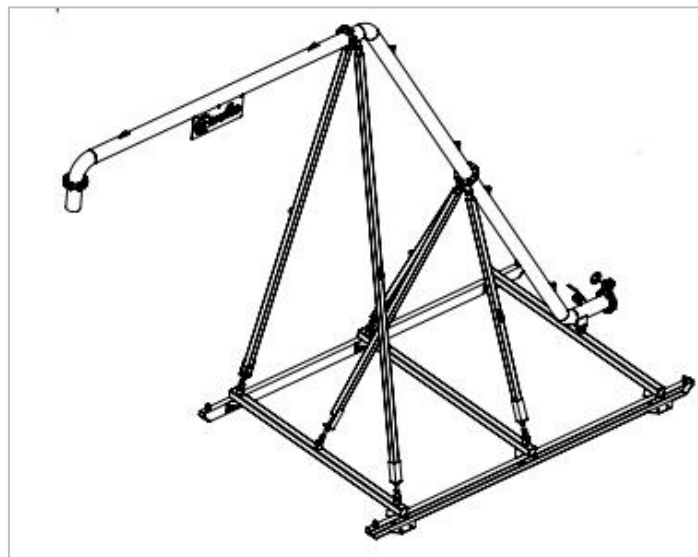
Punto de llenado mediante tubería vertical. [17]
